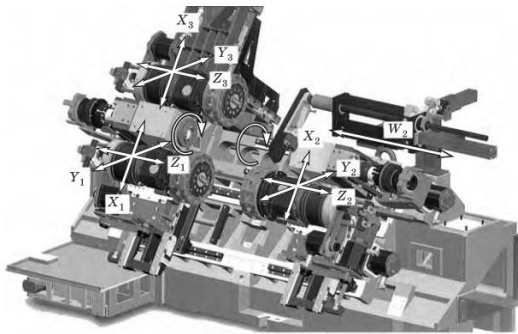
Осі управління токарного багатощпindelного верстата SPRINT 50 фірми DMG
